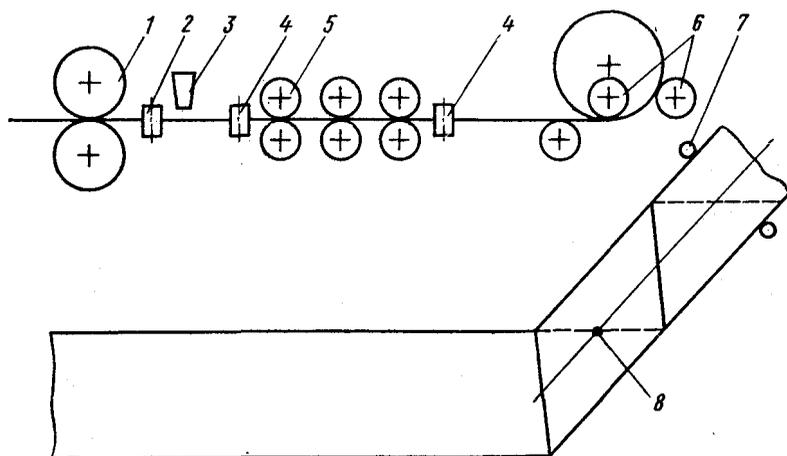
Схема расположения оборудования на участке формовки, сборки и сварки трубы
